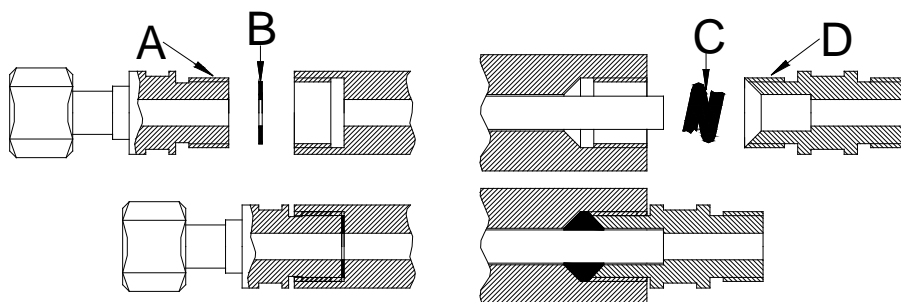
Aufbau Absaugrohre mit festem Innenrohr.
